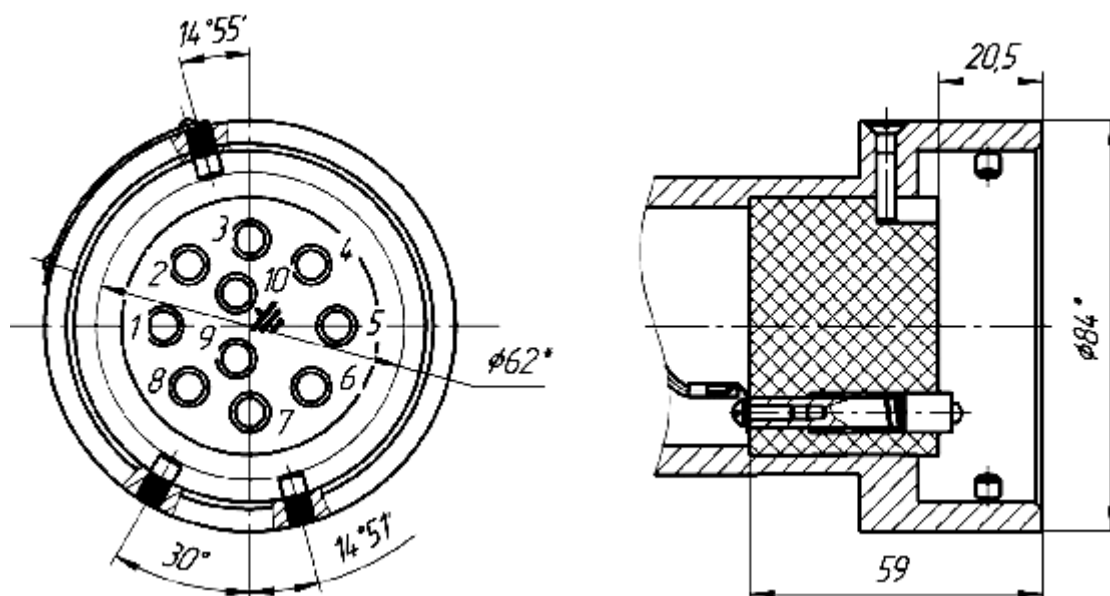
Габаритные размеры и расположение контактов вилки соединительной.
